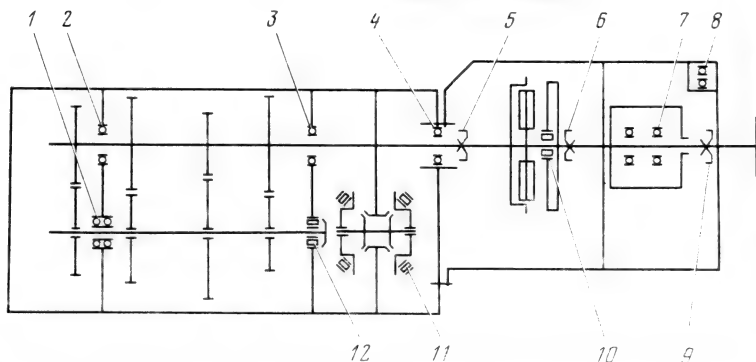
Схема расположения подшипников и манжет силового агрегата
